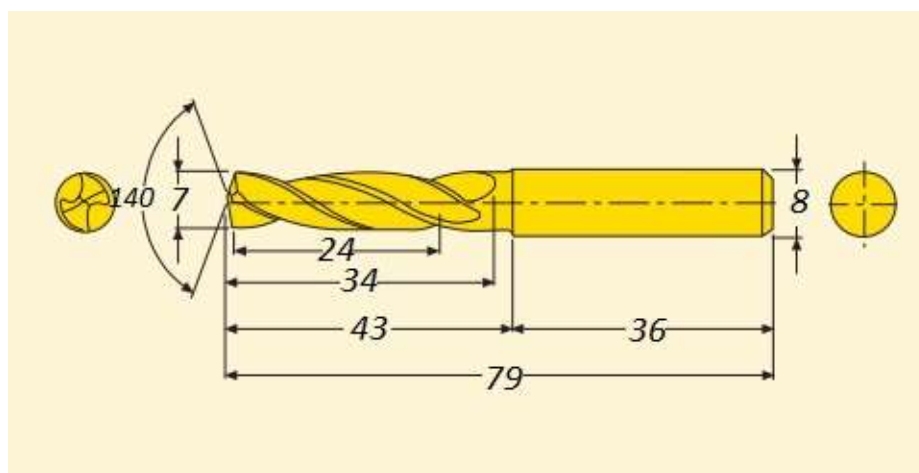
Сверло SecoUniversal – SD1103-0700-024-08R1
